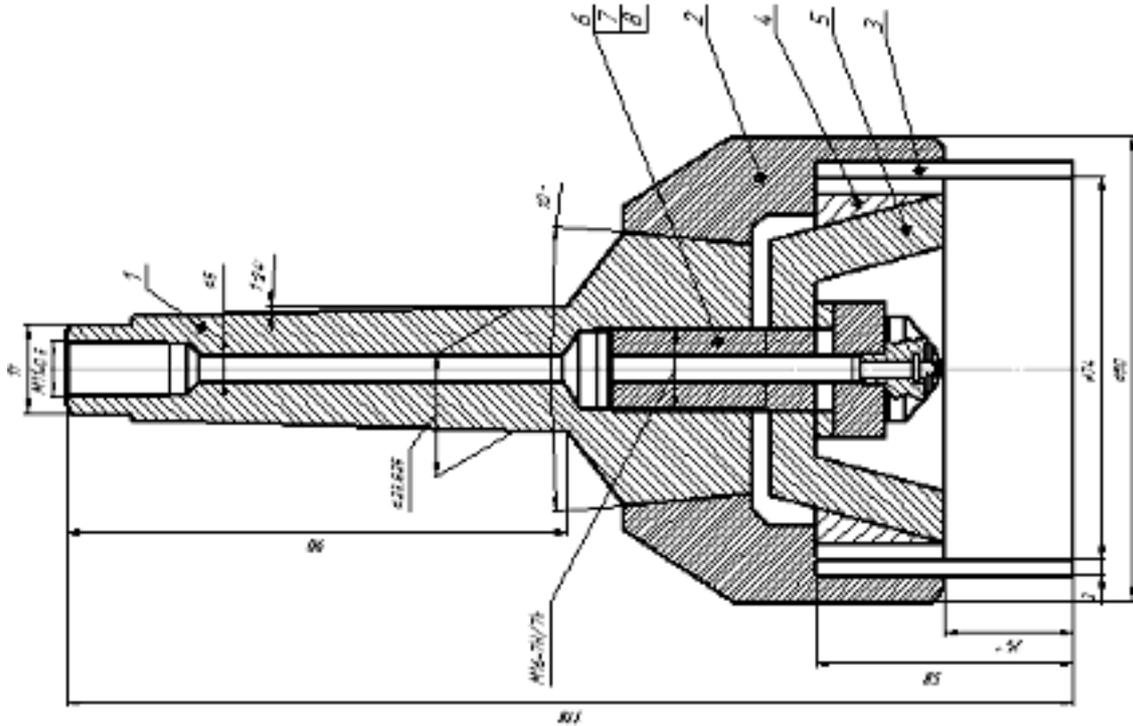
Кольцевое сверло с отверстием для подачи СОЖ:
